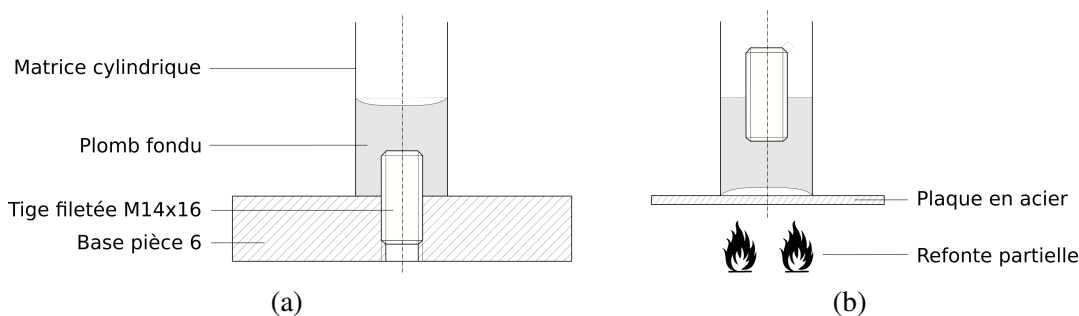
Illustration du principe de fabrication des échantillons en plomb. (a) Moulage initial et (b) refonte de la surface utile.
